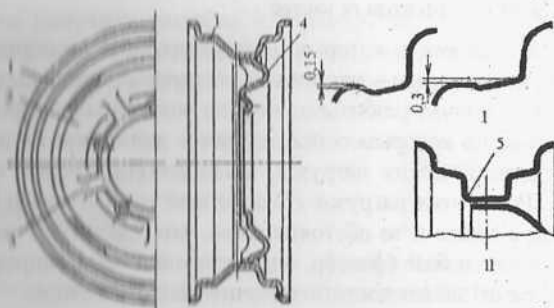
Колесо с глубоким неразборным ободом: I – профили посадочных полоз для бескамерных шин; II – симметричный профиль обода: 1 – обод; 2 – диск; 3 – ребра жесткости; 4 – выступ для крепления декоративного колпака; 5 – монтажный ручей
